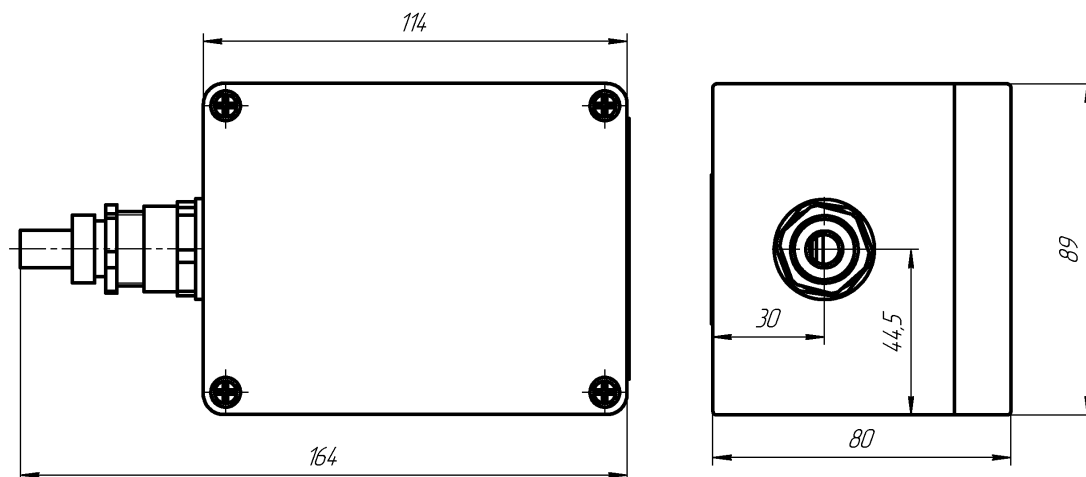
габаритные размеры датчика ДТ-Мх
